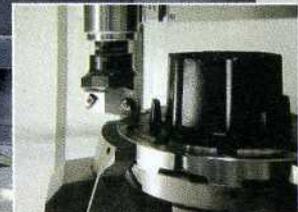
Jeder Maschinenstand der Powerspeed 6 greift auf einen Werkzeugwechsler mit bis zu 150 Werkzeugen zu.
